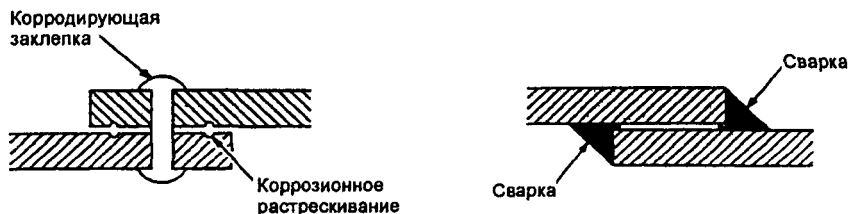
Сварка как способ предотвращения коррозионного растрескивания
